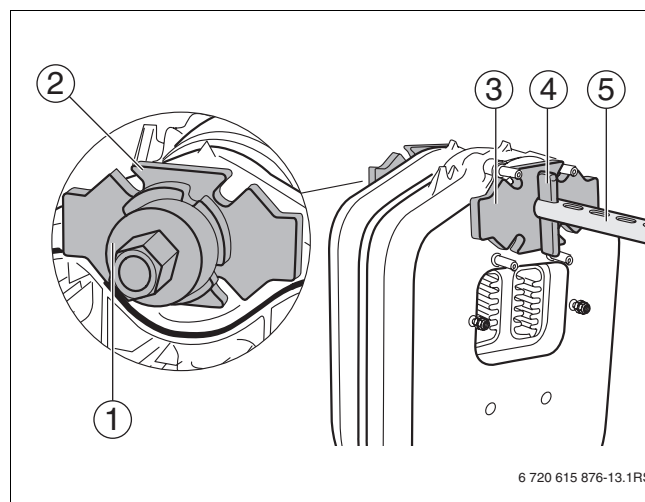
Outil de serrage monté sur le moyeu supérieur
